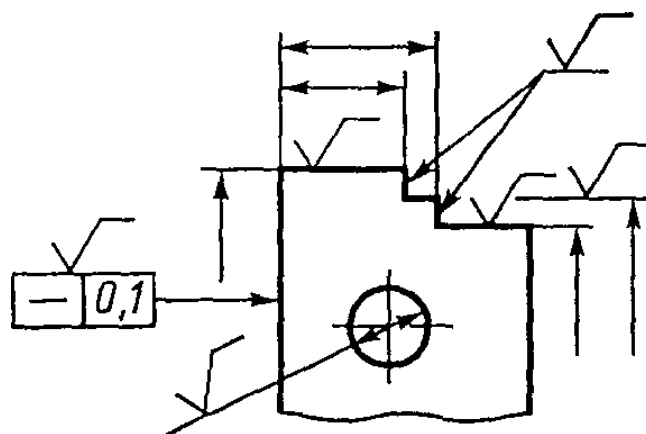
Расположение обозначения шероховатости на размерных линиях
